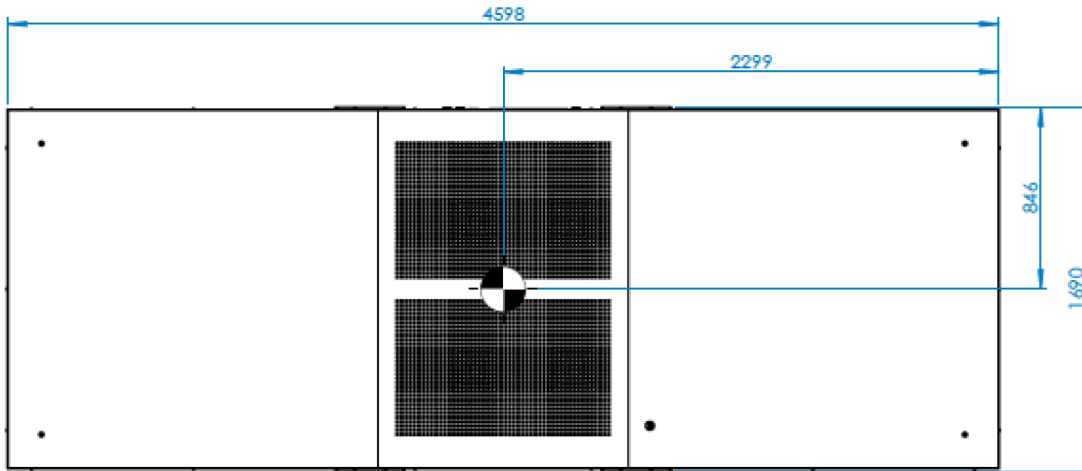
Draufsicht mit Bemaßung und Lage des Schwerpunkts [in mm]
